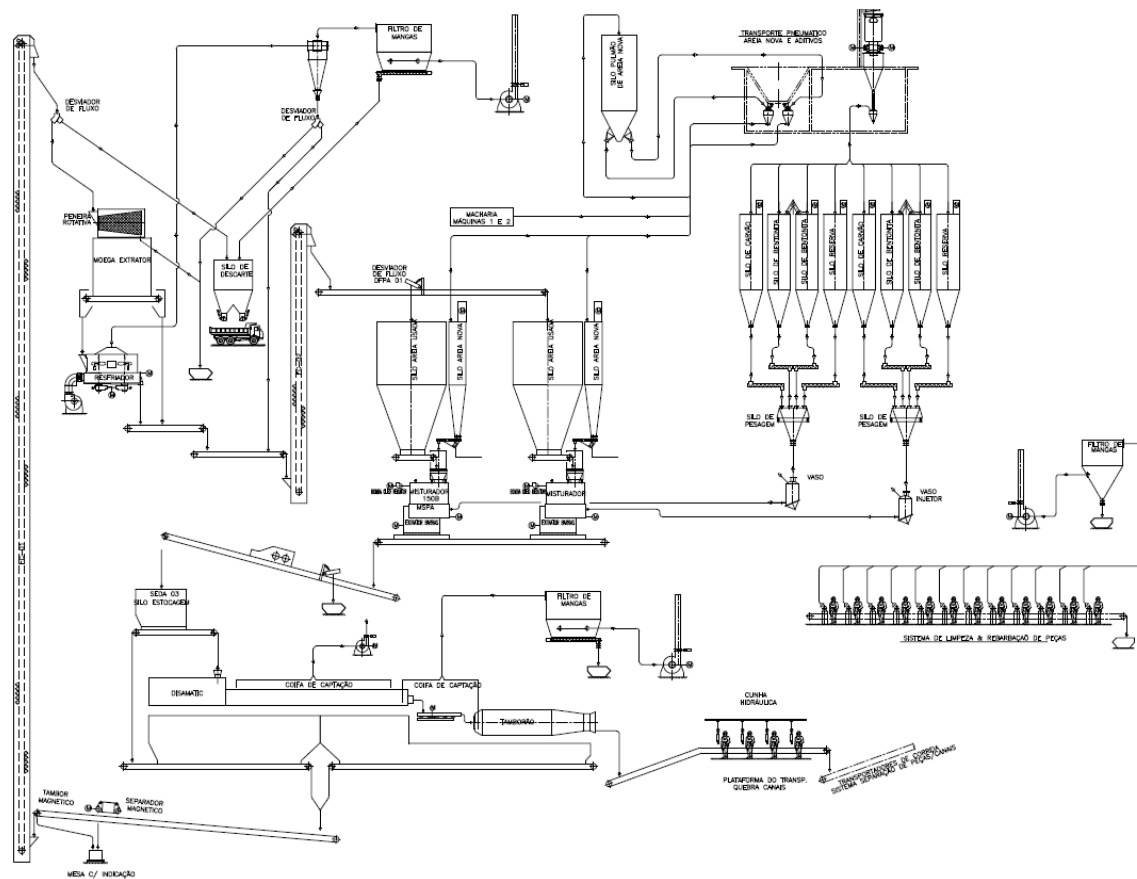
Sistema de limpeza de gases para instalação de moldagem - Fundição
